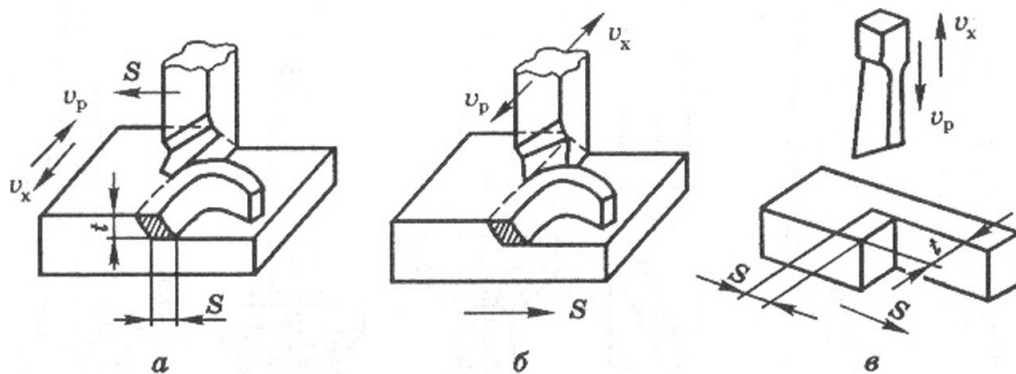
Схеми обробки заготовок на стругальних (а, б) і довбальних (в) верстатах
